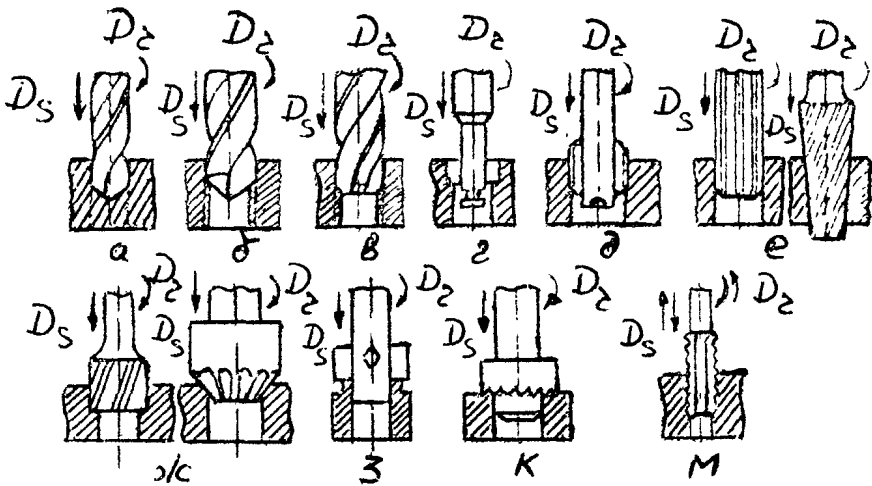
Схеми обробки отворів на свердлильних верстатах
